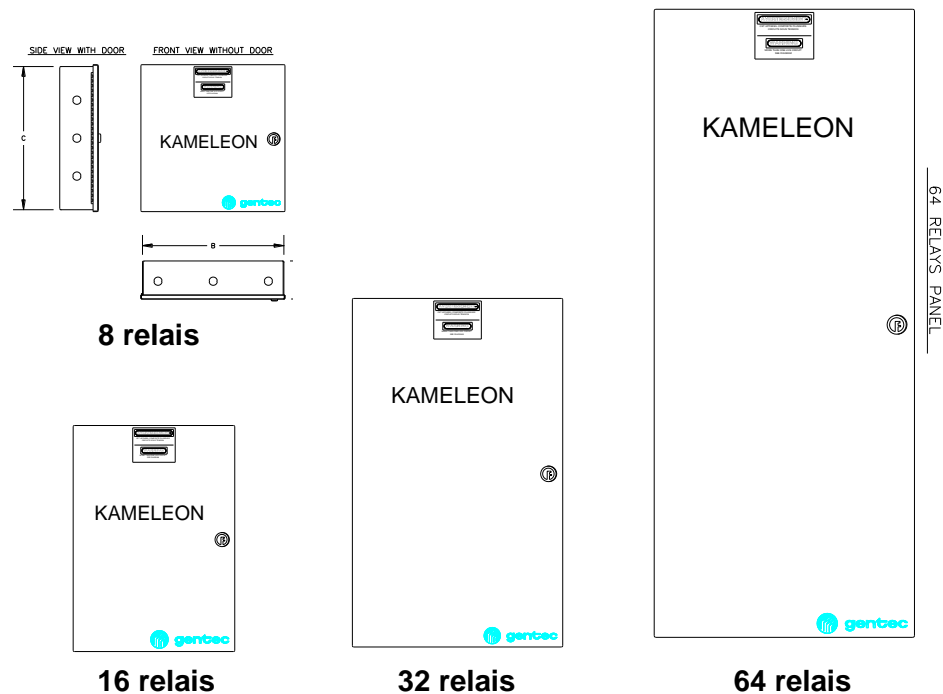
Dimension des panneaux K6-8PA, K6-16PA, K6-32PA et K6-64PA
